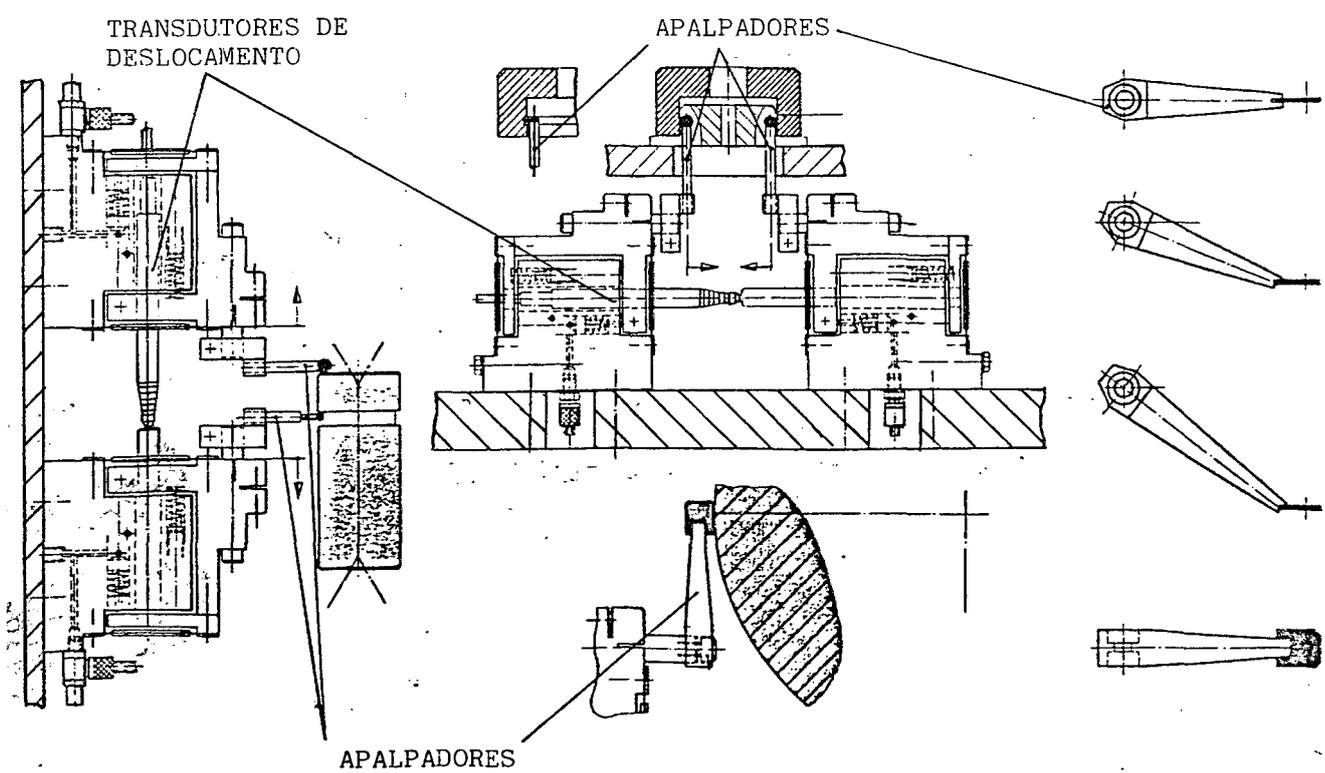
Exemplos de aplicação de apalpadores em dispositivos de medição.
